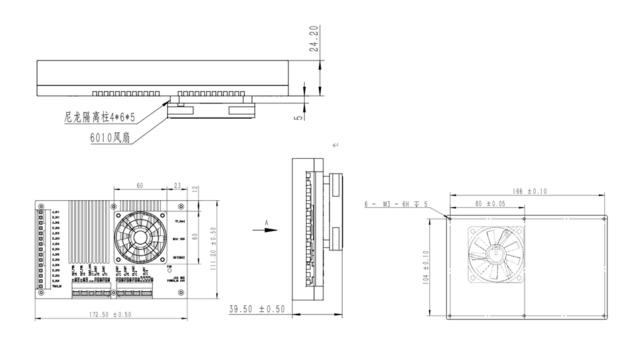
SPCB-NET-B6 外部尺寸图 (单位: mm)
